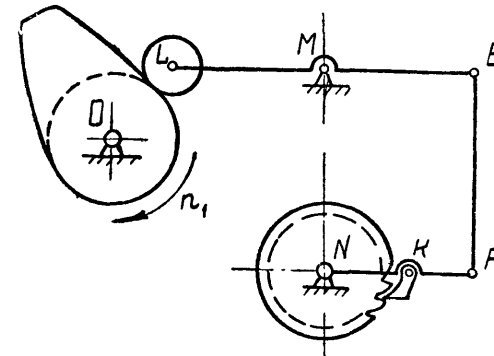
3. Схема кулачкового механизма поперечной подачи стола
